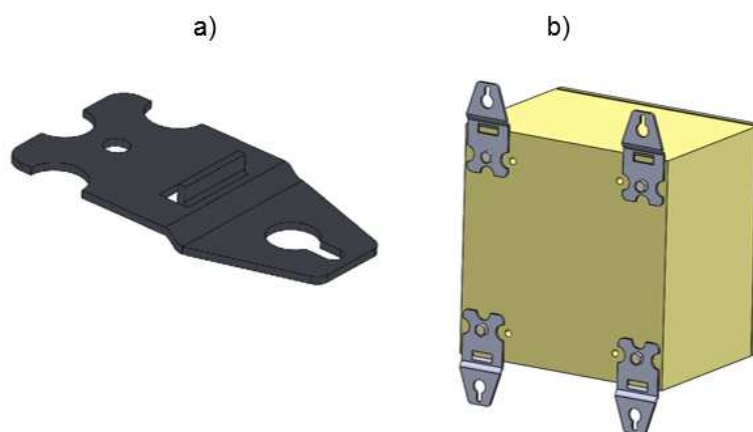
a) Soporte metálico b) Soporte metálico colocado en gabinete
